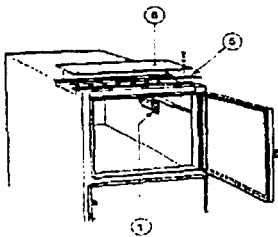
Entrada de cables auxiliares por la parte superior.
